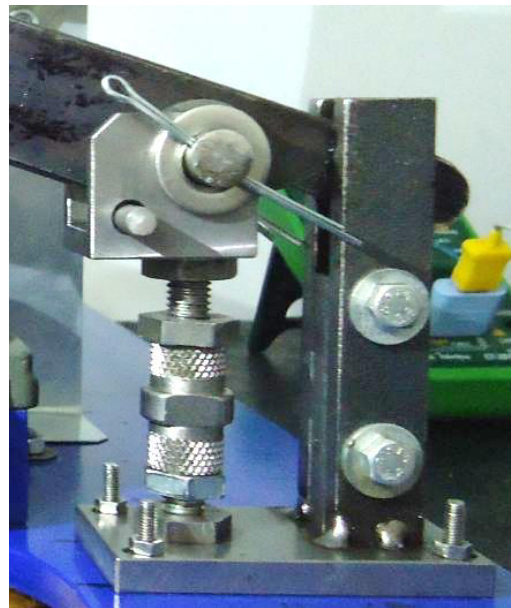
Conjunto de suporte da haste, com regulagem de altura.
